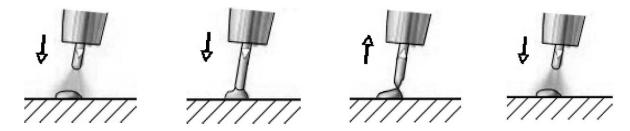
Механизм перехода расплавленной капли металла в сварочную ванну
